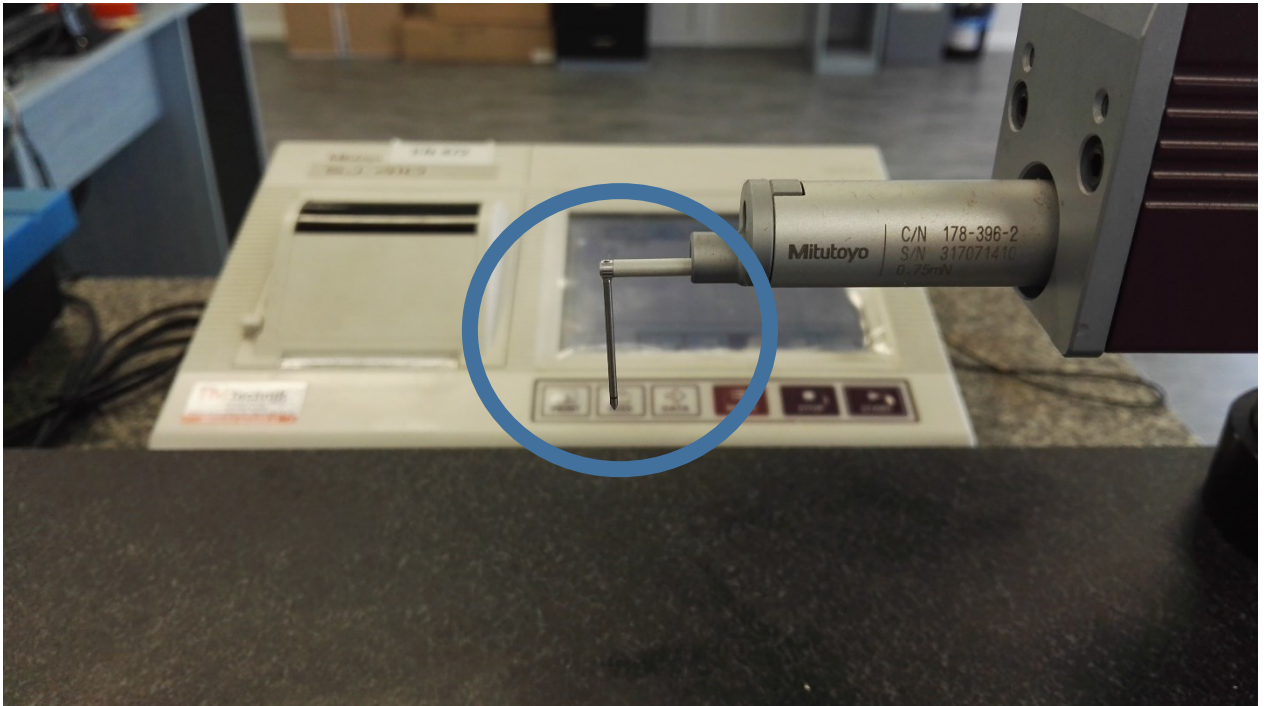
Přístroj Mitutoyo Surftest SJ-410
